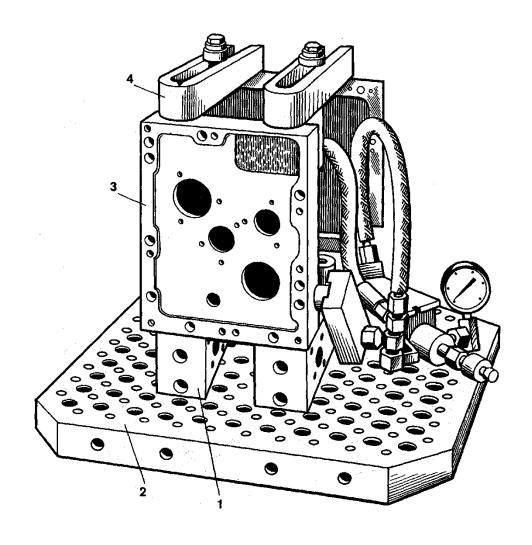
Приспособление двухместное гидравлическое для корпусной детали: 1 - планка, 2 - плита, 3 - заготовка, 4 прихват
